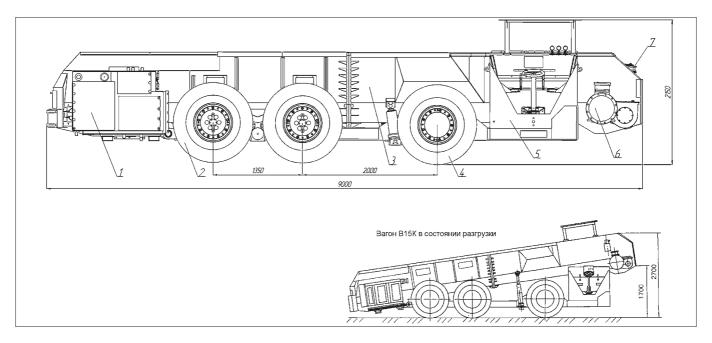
Конструктивная схема вагона пневмоколесного самоходного грузового В15К: I — станция управления; 2 — электромотор-колесо; 3 — кузов; 4 — мост рулевой; 5 — кабина машиниста; 6 — привод конвейера; 7 — выводное устройство кабельного барабана
